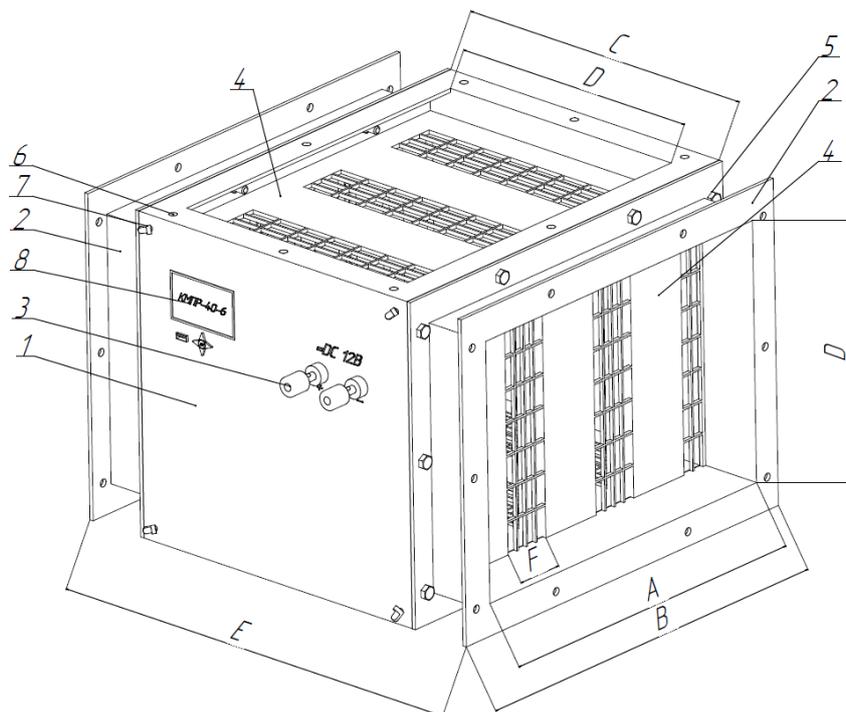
Многослойный пластинчатый рекуператор (общий вид): 1 – съемная крышка; 2 – фланец; 3 – клеммы подключения нагрузки; 4 – решетка; 5 – болтовое соединение; 6 – отверстия для подключения к воздуховодам; 7 – крепление боковых стенок
